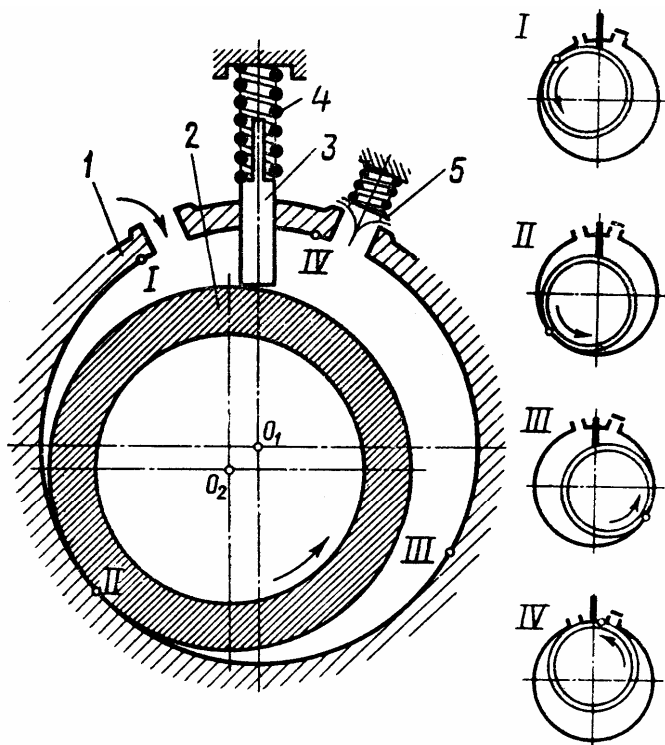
Схема ротаційного компресора з ротором, що котиться
